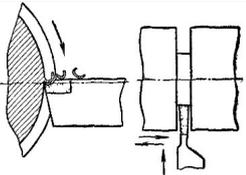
Отрезной резец с напаянной пластинкой из твердого сплава конструкции П. Я. Мехоциева
